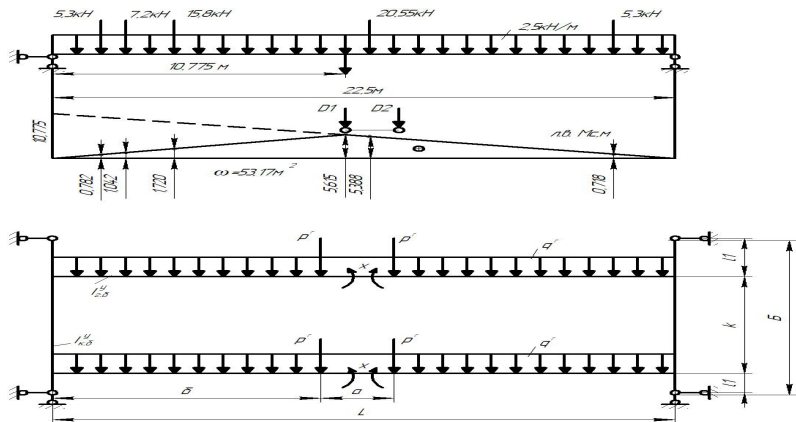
Расчетная схема моста крана при расчетах на горизонтальные нагрузки.
